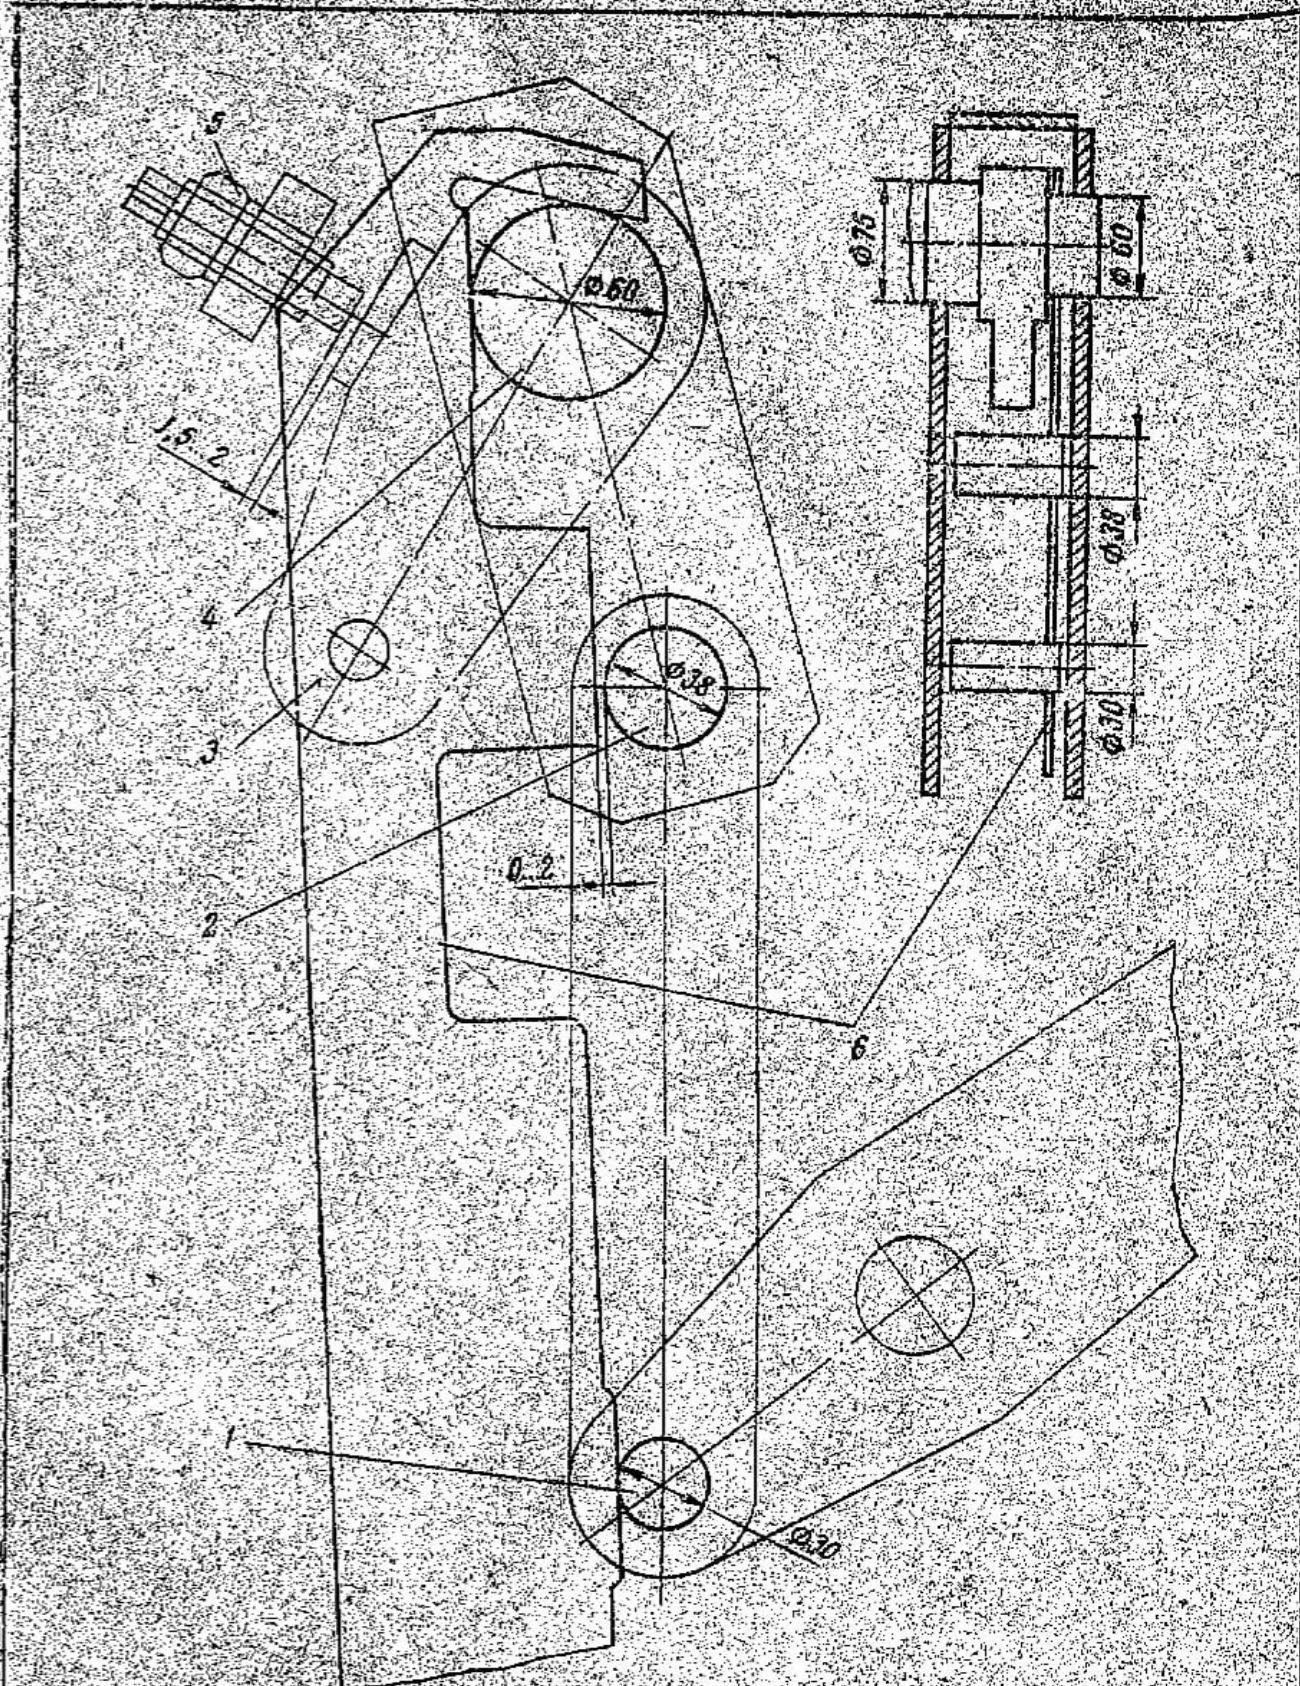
Схема проверки шаблоном включенного положения рычагов механизма.
